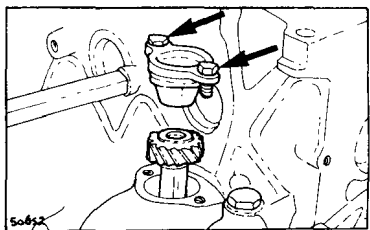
Крышка-заглушка шестерни привода масляного насоса
